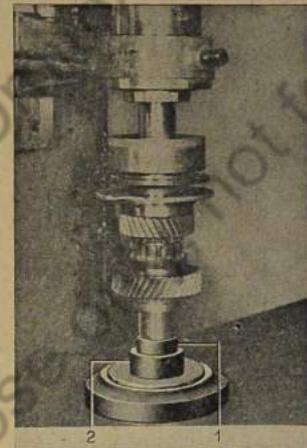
Laufbuchse zum Schrägrad für 2. Gang aufpressen
